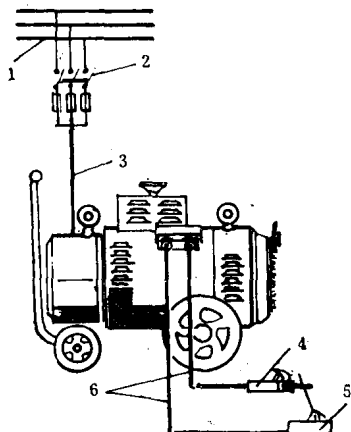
AX-320 型直流弧焊机的外部连线
